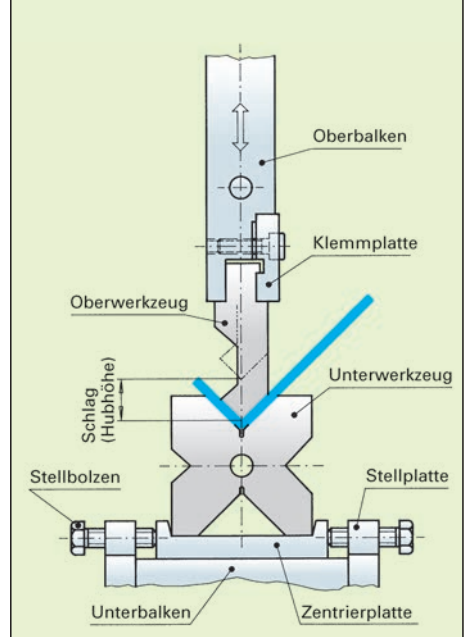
zeigt das Kernstück jeder Gesenkbiegepresse – den auswechselbaren Oberstempel, auch Schwert genannt – sowie das schwenkbare Prisma. Die Kröpfung des Schwerts ist für Zargen und Mehrfachkantungen notwendig (siehe Arbeitsbeispiele S. 49, Bild 1).
